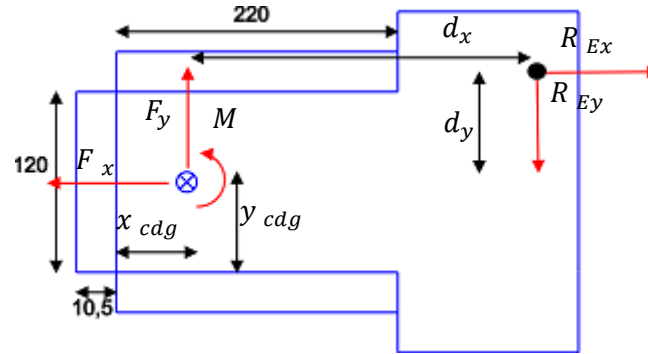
(1): Geometría de los cordones de soldadura
